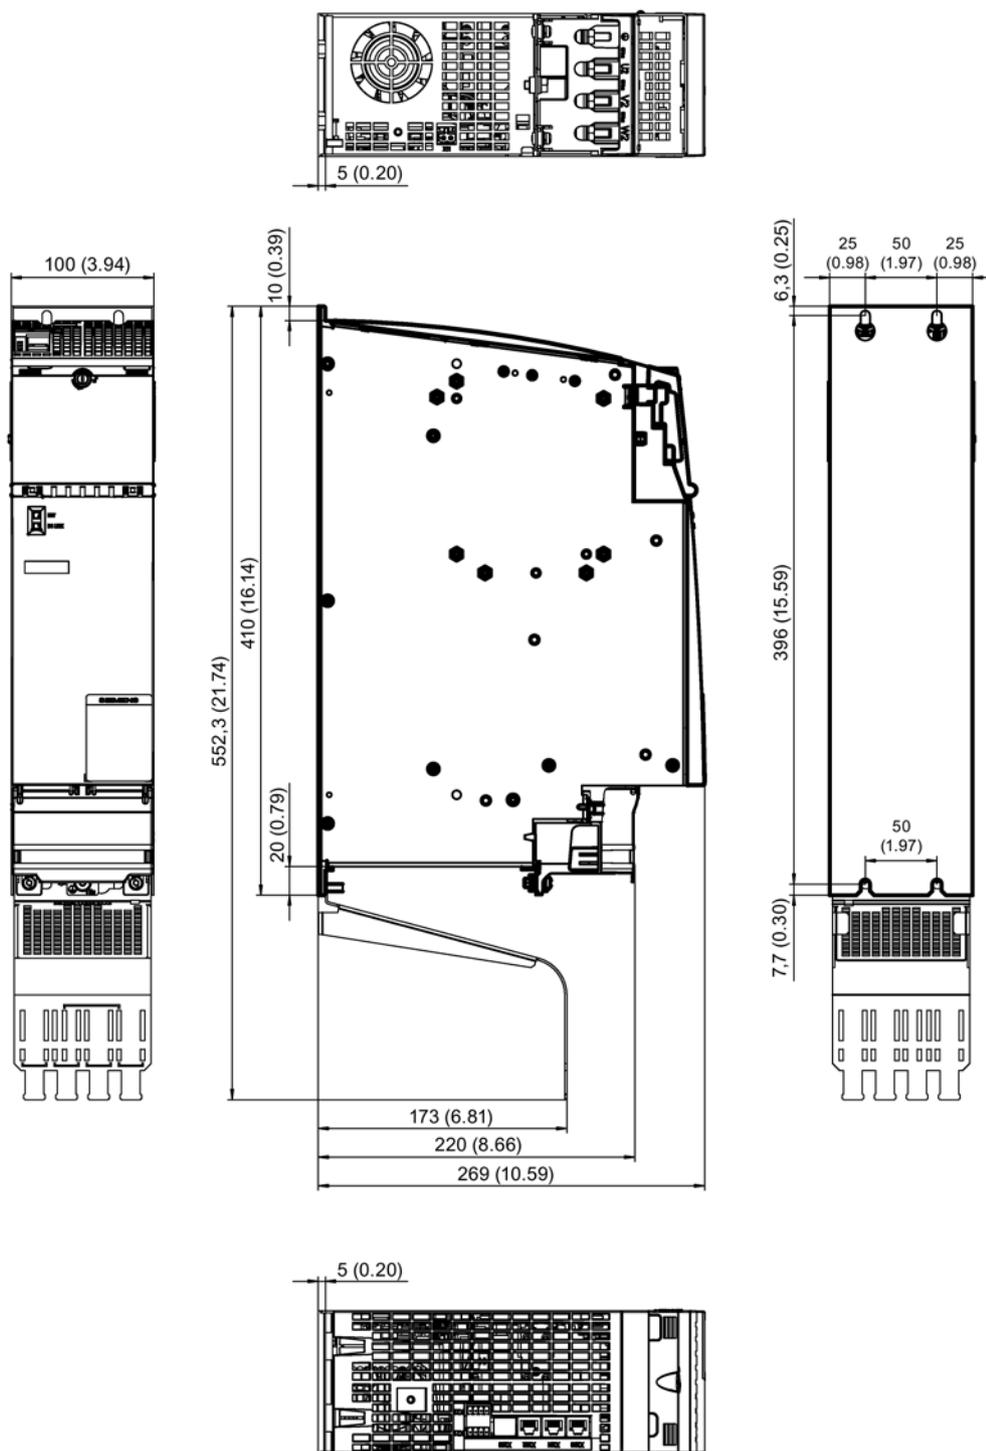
Croquis acotado de Motor Modules Booksize C-Type con refrigeración por aire interna de 100 mm 45 A/60 A, todas las medidas en mm y (pulgadas)
